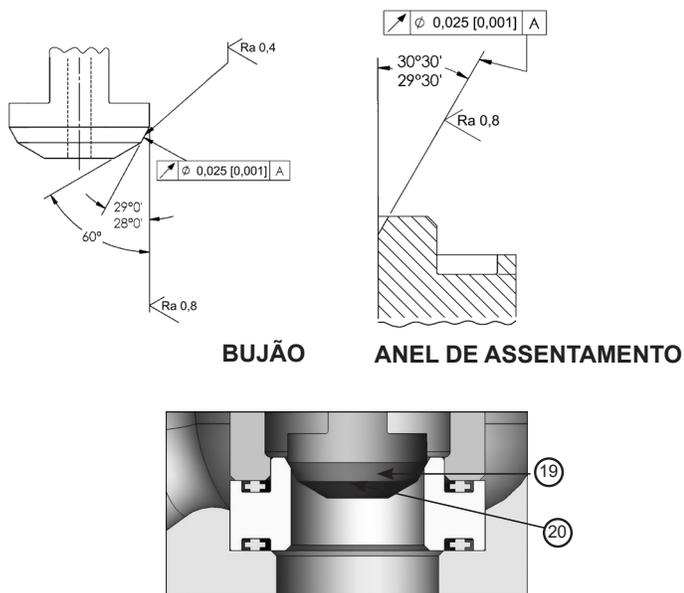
Superfícies de assentamento do bujão e do anel de assentamento
